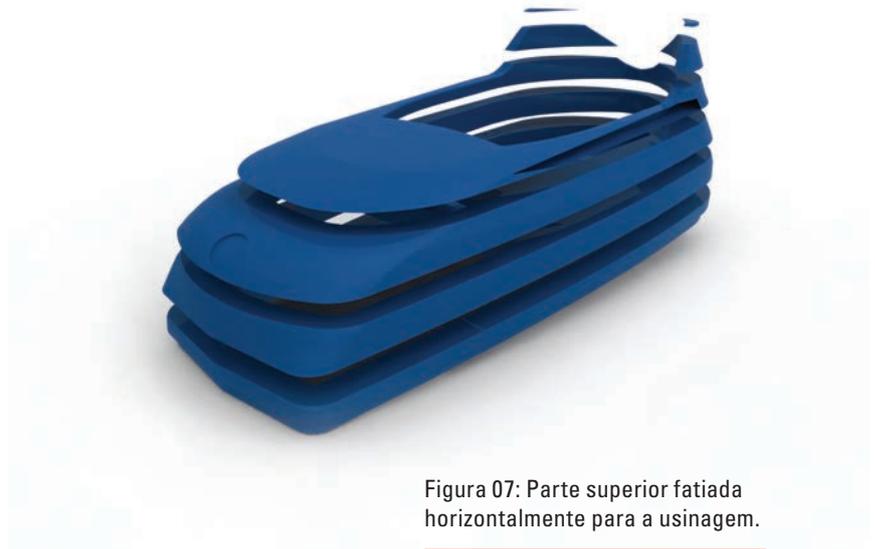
Parte superior fatiada horizontalmente para a usinagem.
